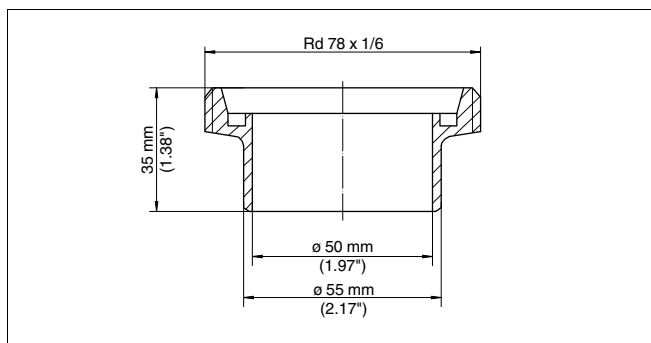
Medidas da luva soldada união roscada para tubo DN 50 conforme DIN 11851
